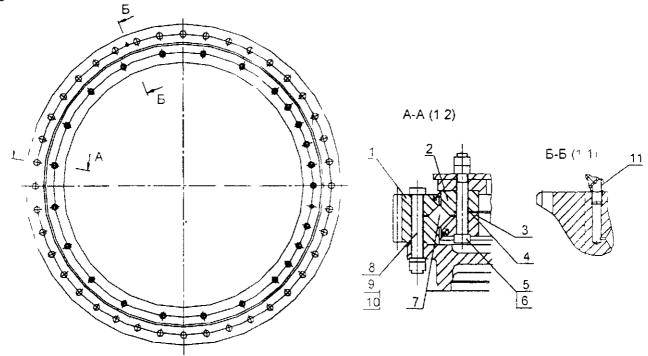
Опора поворотная 1 зубчатый венец; 2, 3-полуобоймы; 4-прокладка; 5, 8-болты; 6,9-гайки; 7-ролик; 10-шайба; 11-масленка
